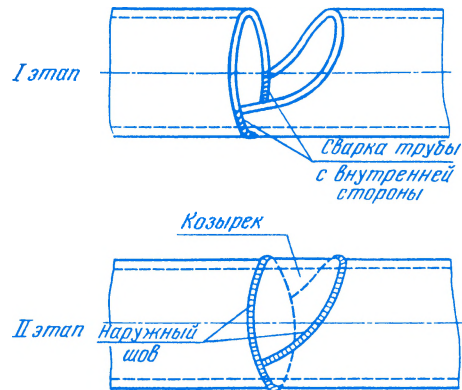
Порядок сварки стыков труб с козырьком
